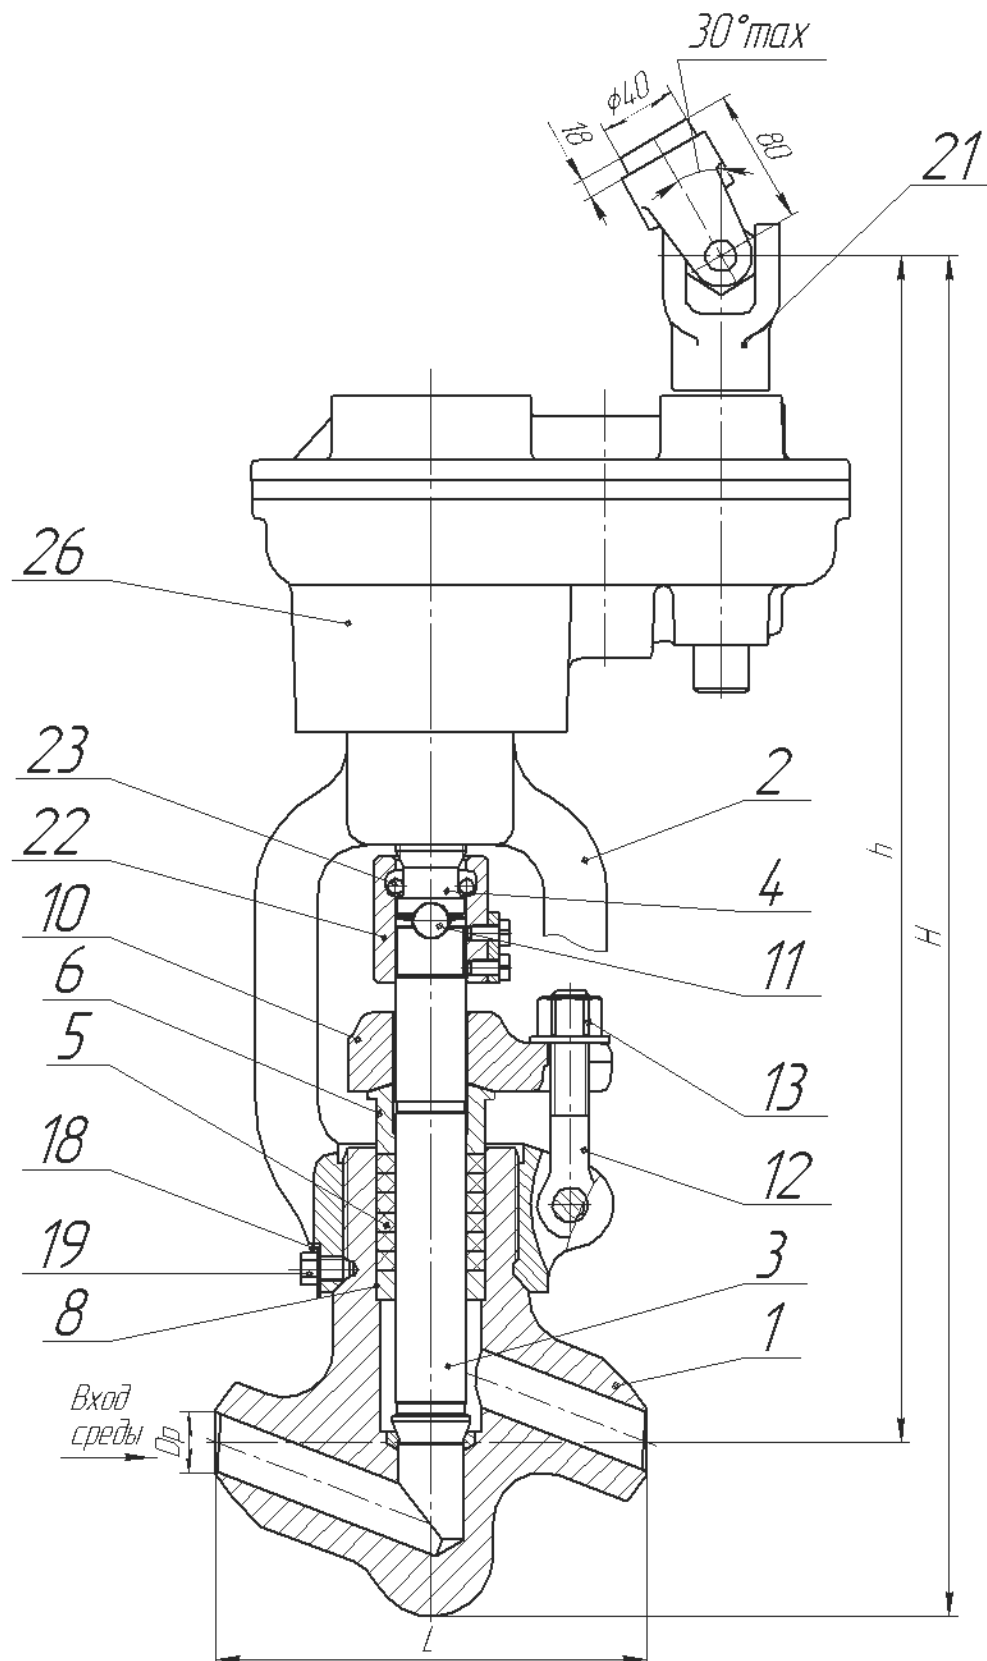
Клапан запорный DN32-65 с цилиндрическим редуктором
